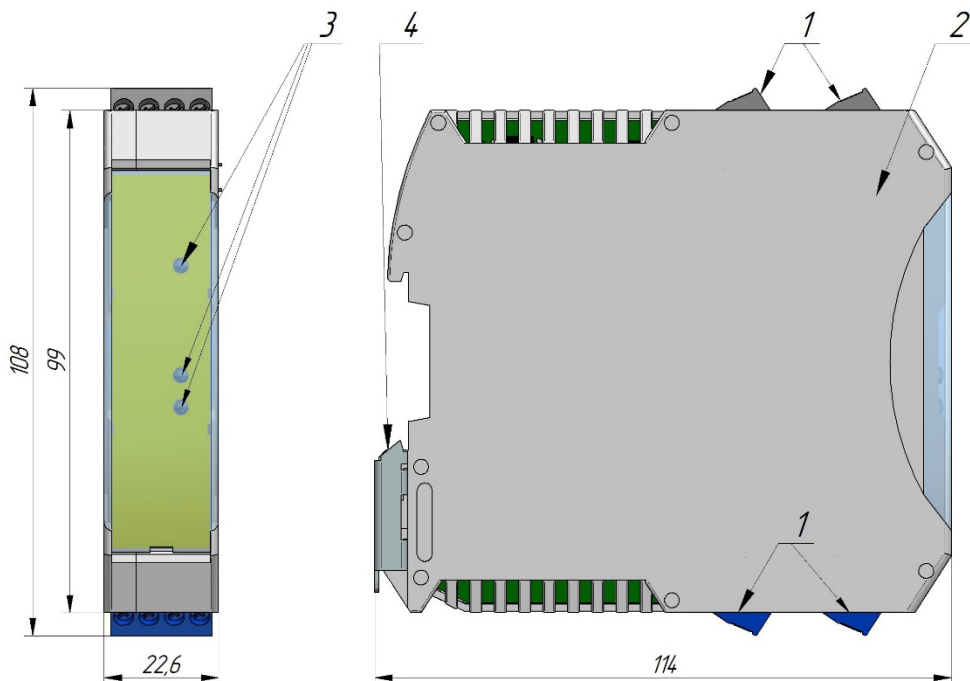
Внешний вид и габаритные размеры РБ1
